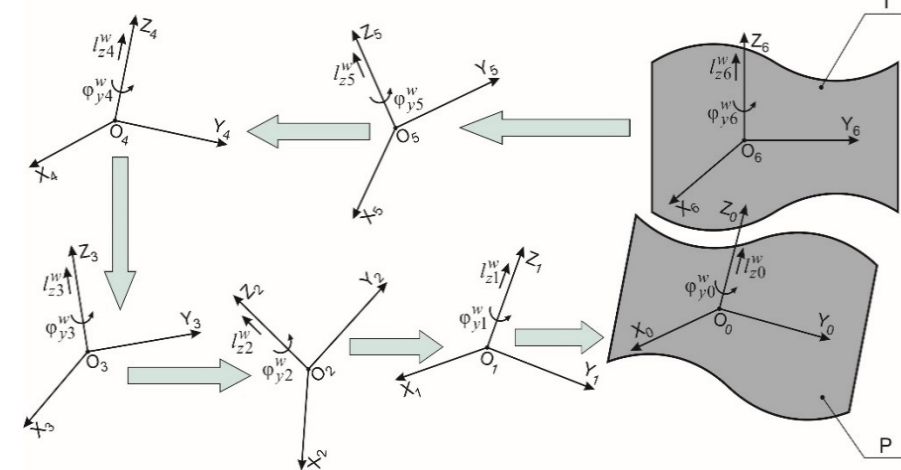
Схема области существования обобщенной кинематической схемы формообразования зубчатых звеньев различных классов, типов и видов: Т – формообразующее зубчатое звено; Р – формообразуемое зубчатое звено
